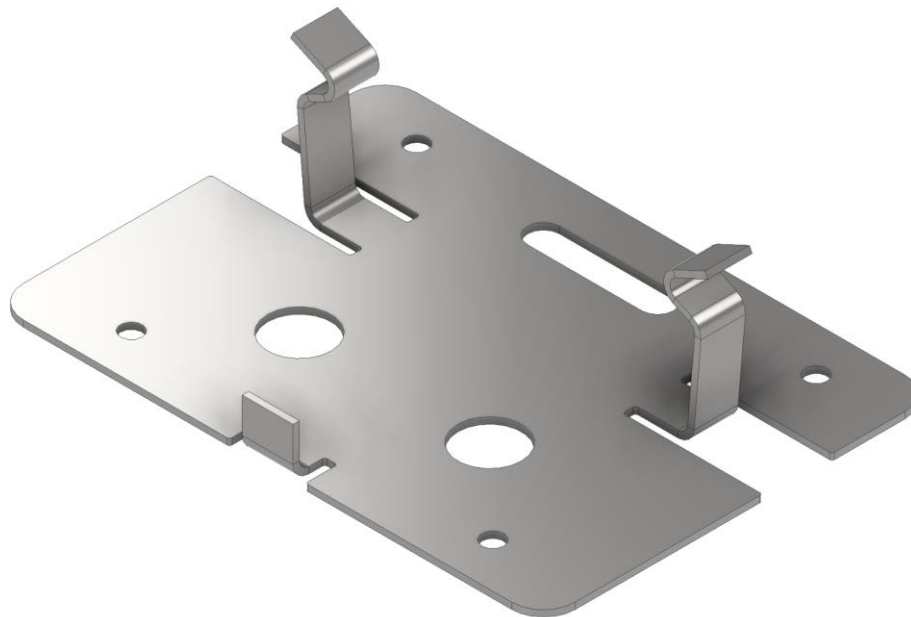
Příklady součástí vyrobených ve sruženém nástroji [2].
